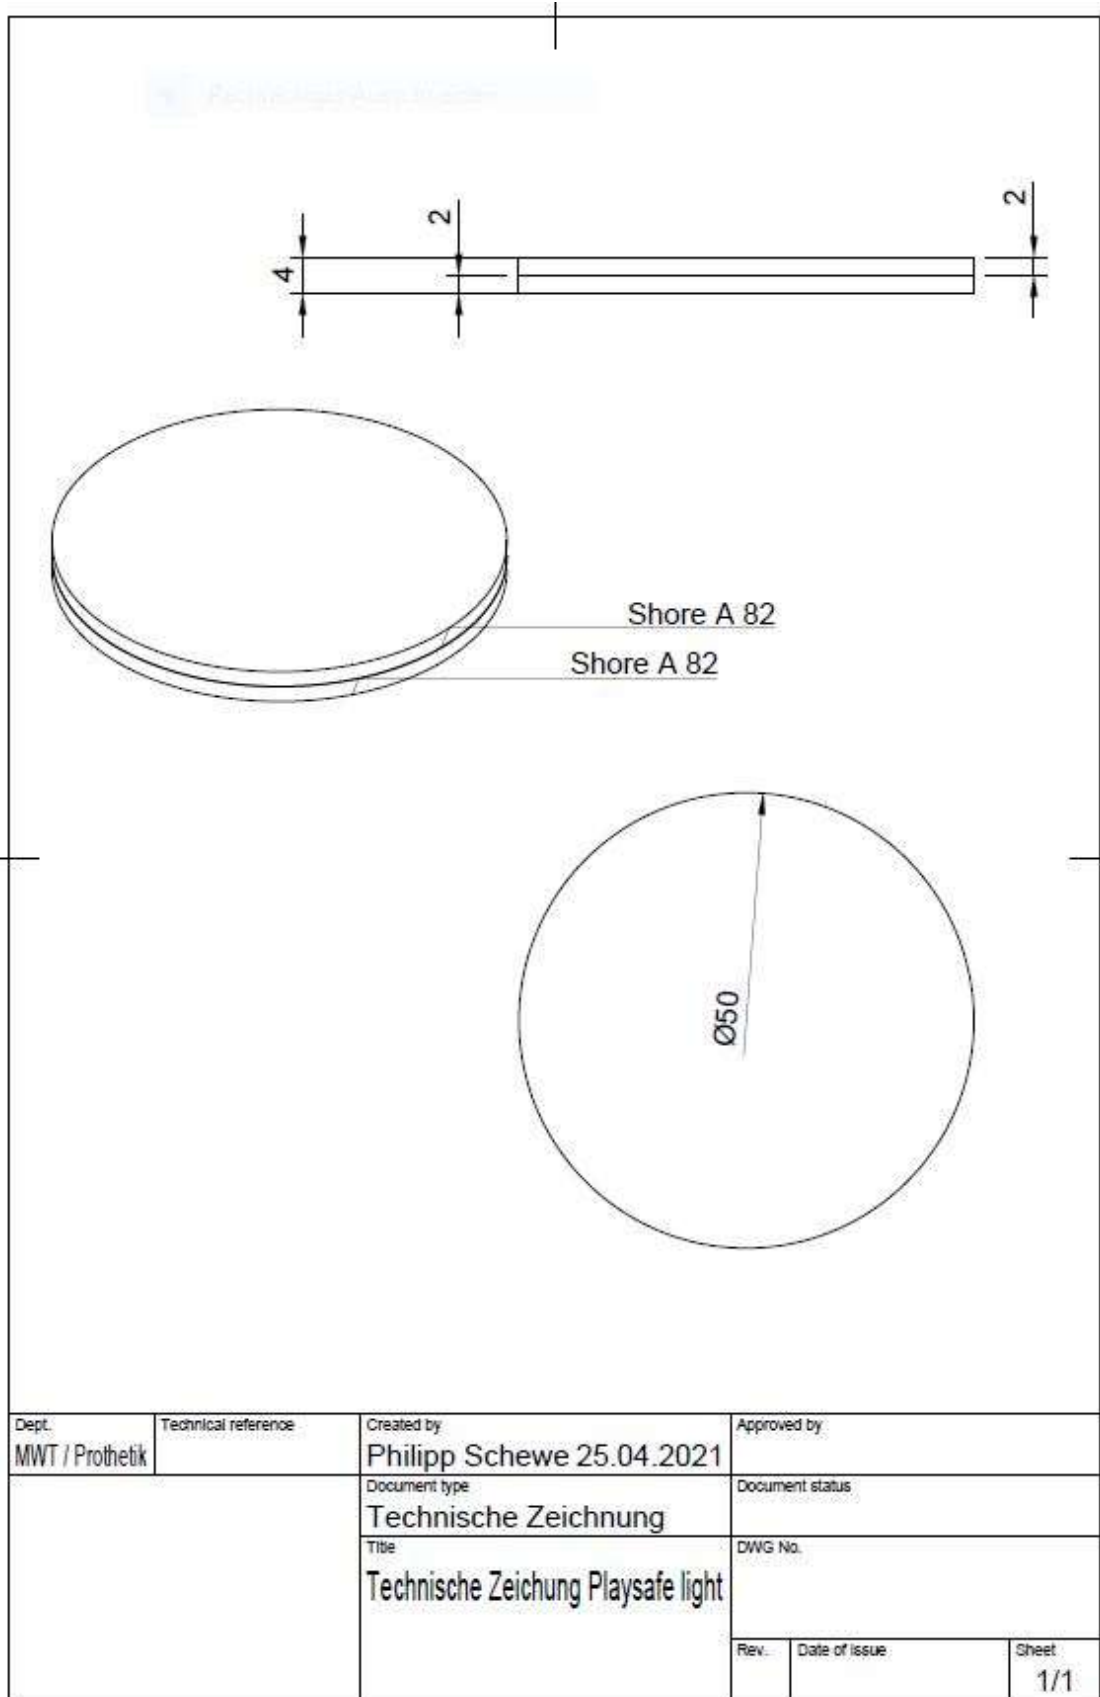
Technische Zeichnung der Materialprobe ER-Li / STR-A
